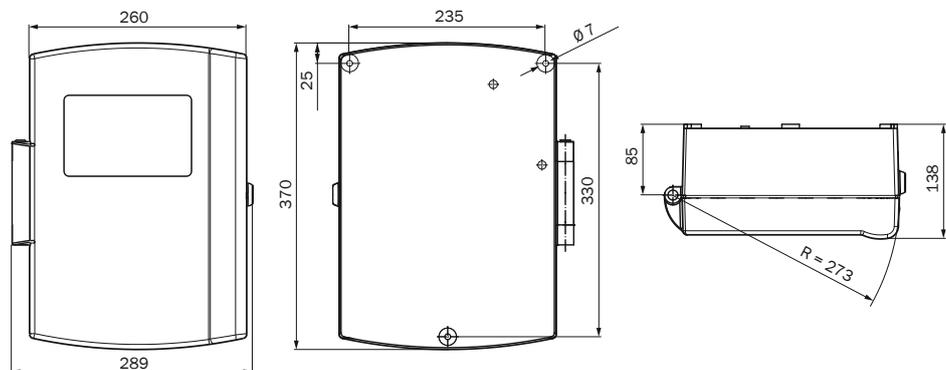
Steuereinheit AWE (Ausführung Metallgussgehäuse), Maße in mm
